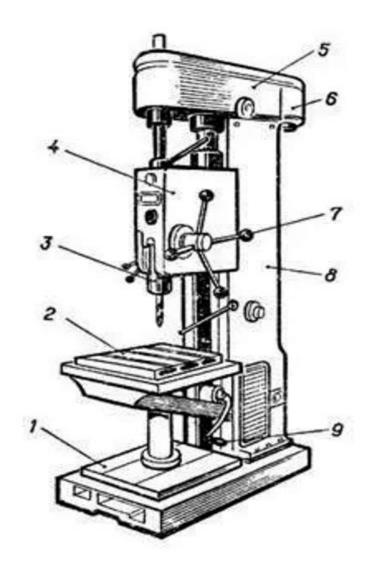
Вертикально-сверлильный станок 2A125: 1 — основание; 2 — стол; 3 — шпиндель; 4 — сверлильная головка; 5 — коробка скоростей; 6 — электродвигатель; 7 — коробка подач; 8 — колонна; 9 — рукоятка перемещения стола
